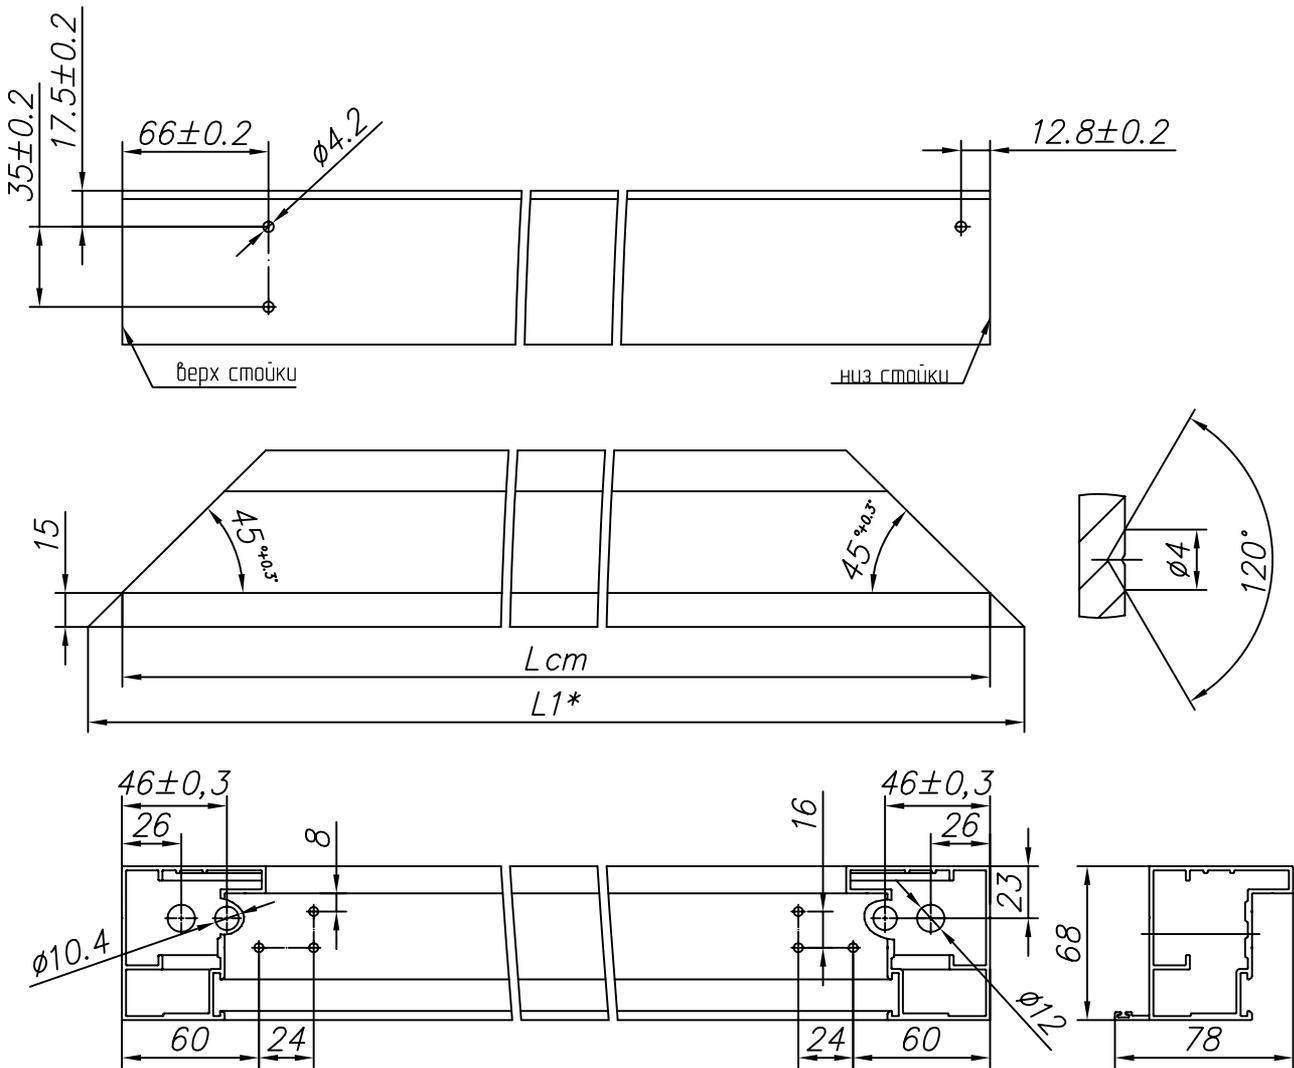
Изготовление стойки из профиля FLGU.400.0110 (стойка левая, открывание калитки внутрь)
